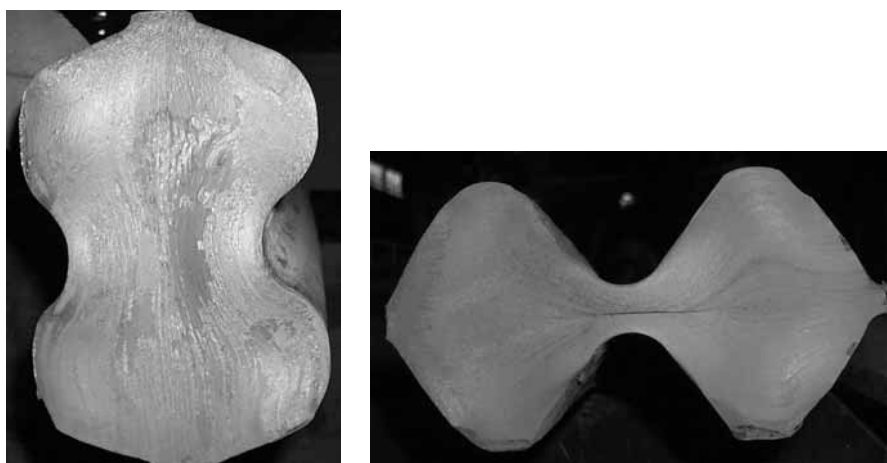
Внешний вид поперечного сечения заготовки при разделении (2-слиттинг)
